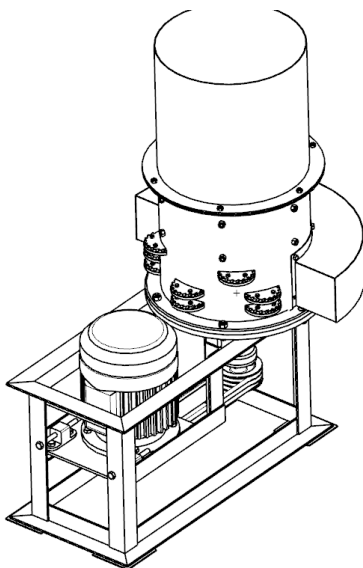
Конструкция роторно-ножевой дробилки ударного типа с многолезвийными рабочими органами
